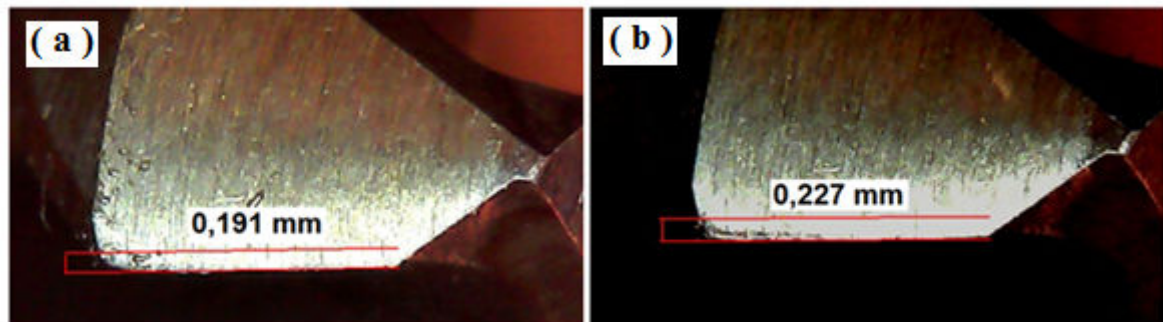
Desgaste de flanco das brocas com AlCrN desgastadas: (a) comprimento usinado de 3072 mm, (b) comprimento usinado de 4608 mm
